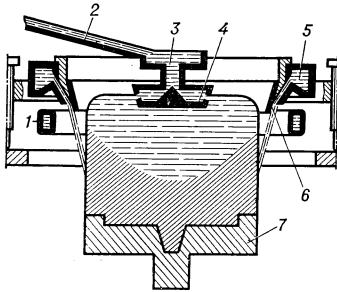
Схема непрерывного литья в электромагнитный кристаллизатор: 1 — индуктор; 2 — лоток; 3 — распределительная коробка; 4 — плавающая чаша; 5 — коллектор; 6 — направляющий конус; 7 — поддон.
